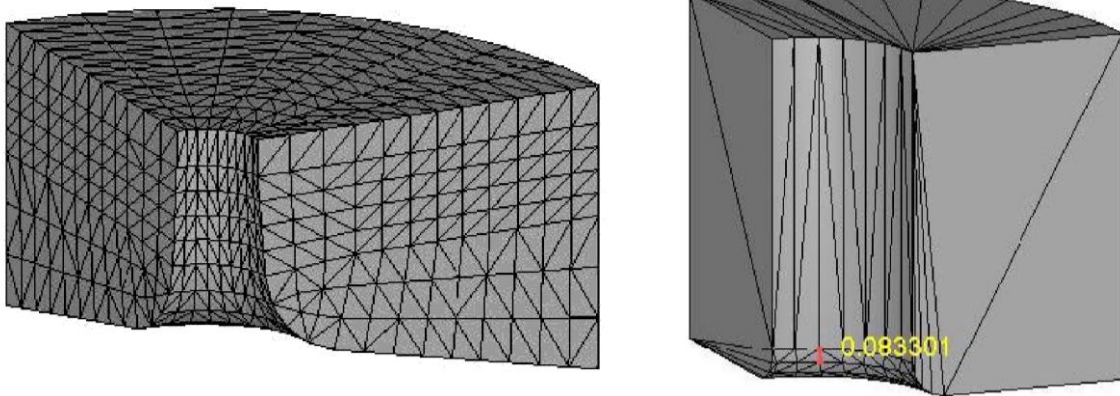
Нанесення розрахункової ґратки на верхню частину штампа.
